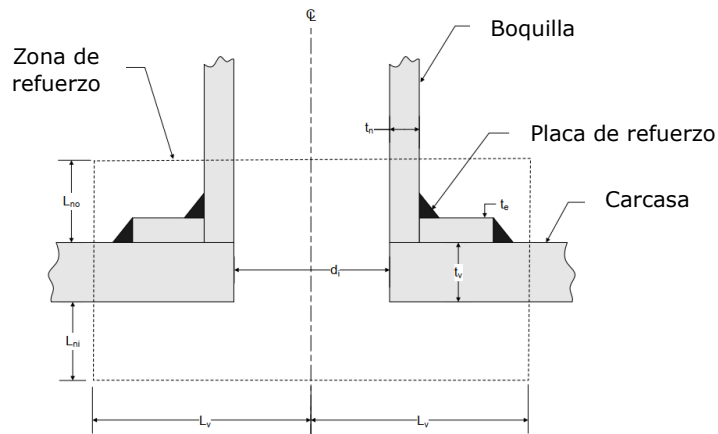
Zona de refuerzo requerida para boquillas con o sin pad de refuerzo.
